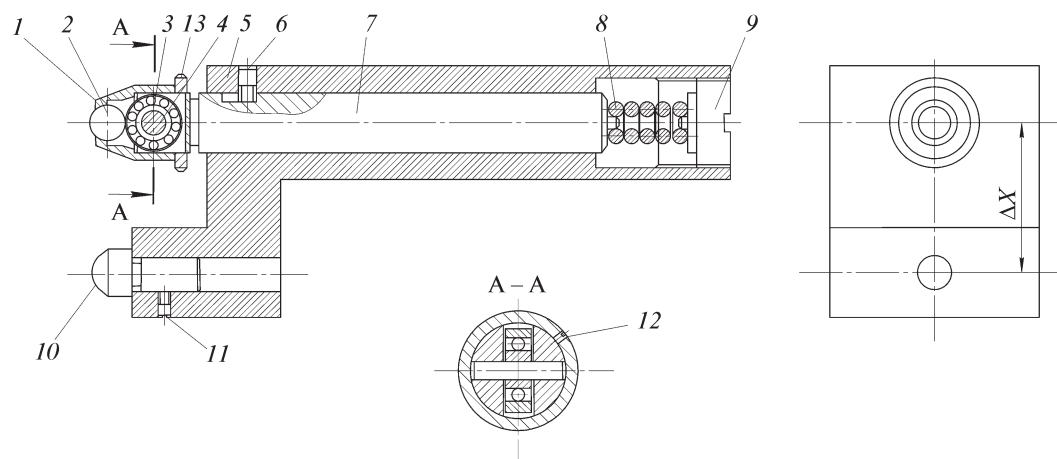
Инструмент для отделочно-упрочняющей обработки
